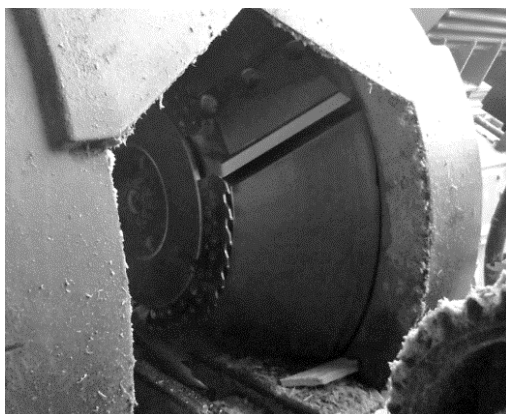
Малоножевая торцово-коническая фреза фрезерно-брусующего станка
